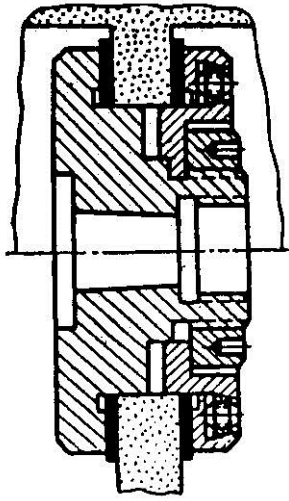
Кріплення шліфувального круга в перехідних фланцях
